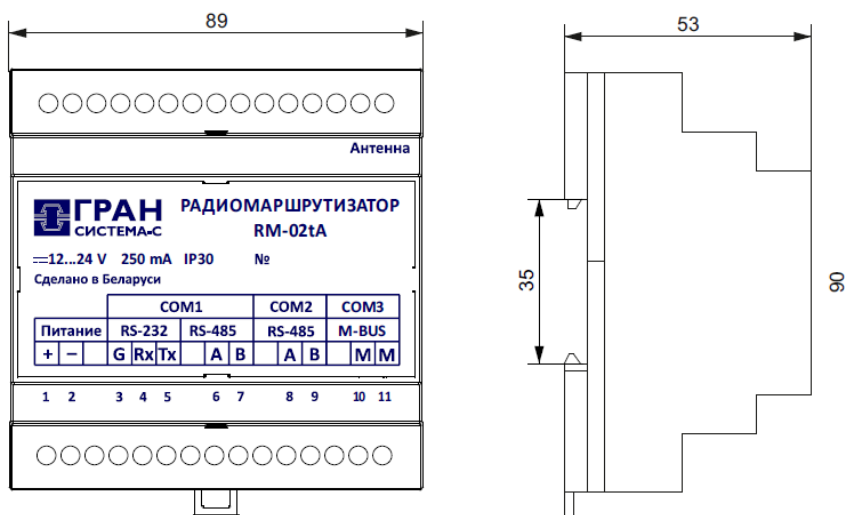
Внешний вид, габаритные и установочные размеры радиомаршрутизаторов RM-02XX
